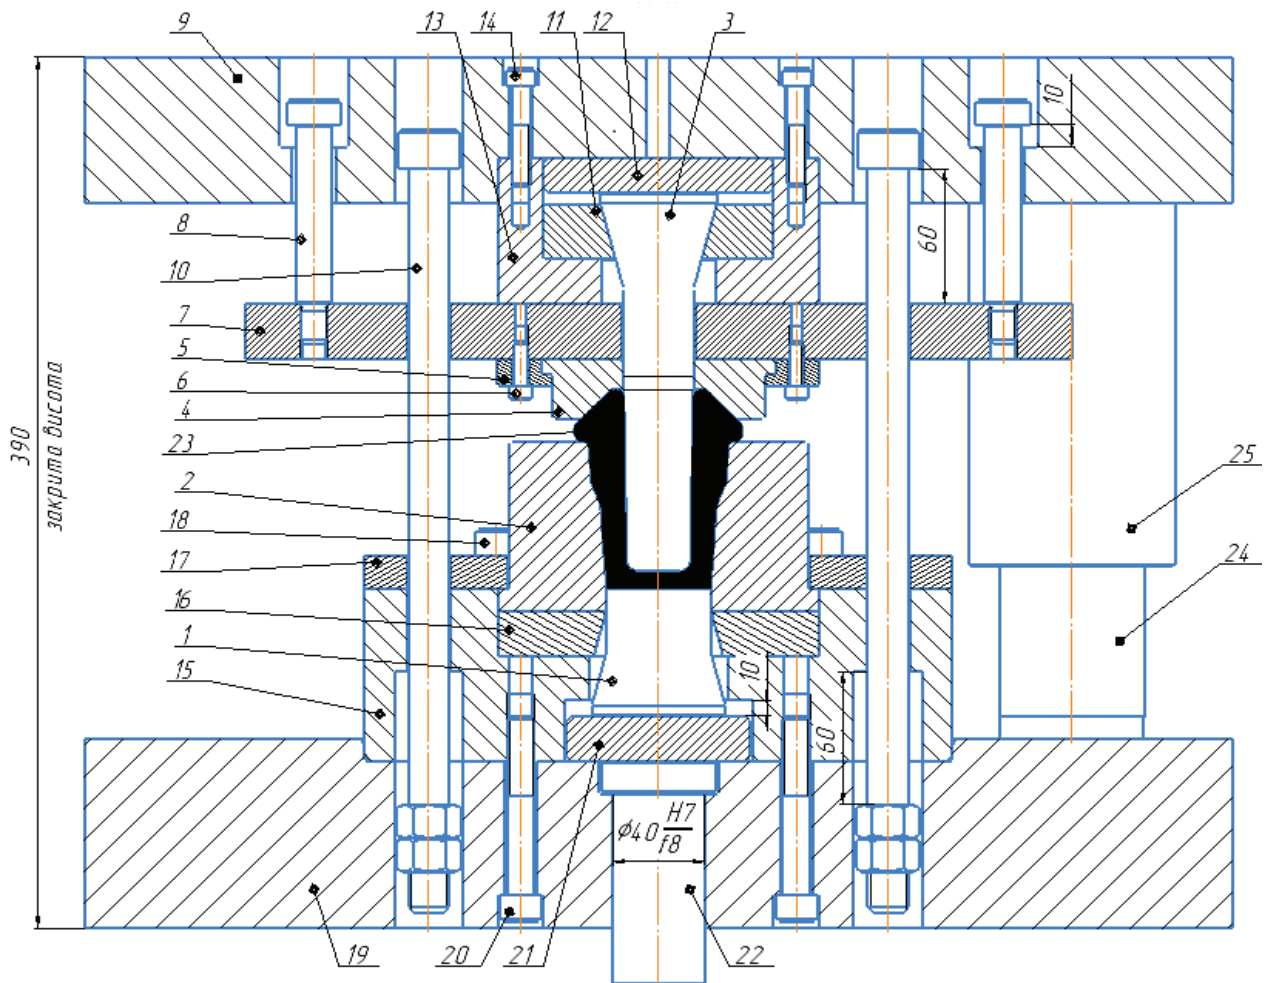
Принципова схема штамп: 1 – виштовхувач; 2 – матриця; 3 – пуансон; 4 – матриця верхня; 5 – тримач верхній; 6 – гвинт; 7 – плита рухома; 8 – гвинт упорний; 9 – плита верхня; 10 – тяга; 11 – шайба опорна; 12 – плита підкладна; 13 – пуансонотримач; 14 – гвинт; 15 – обойма; 16 – опорна плита нижня; 17 – тримач матриці; 18 – гвинт; 19 – плита нижня; 20 – гвинт; 21 – опора; 22 – виштовхувач; 23 – напівфабрикат; 24 – колонка направляюча; 25 – втулка направляюча
